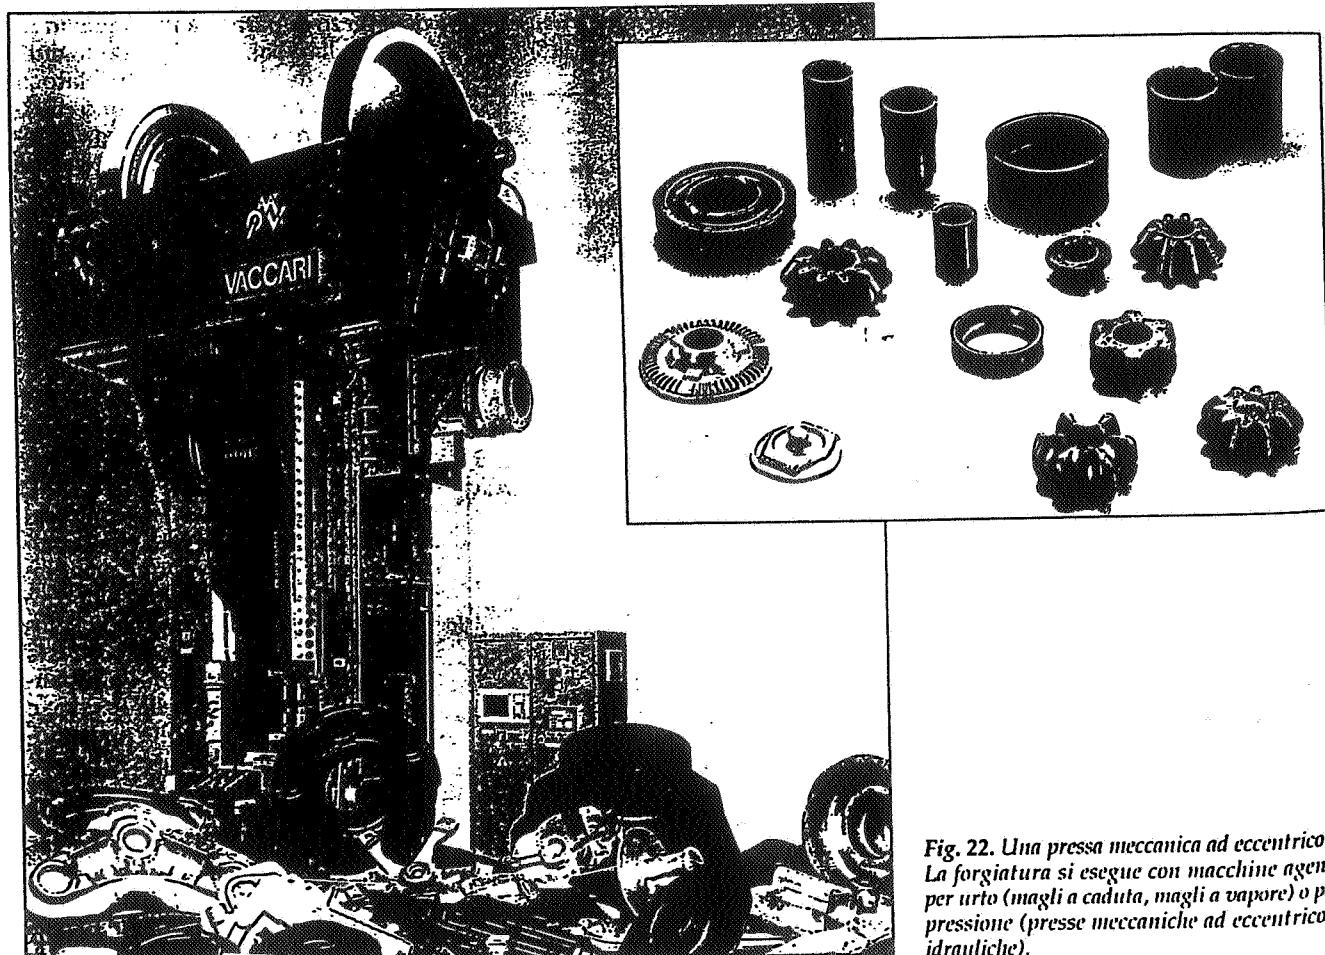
Una presa meccanica ad eccentrico. La forgatura si esegue con macchine agenti per urto (magli a caduta, magli a vapore) o per pressione (presse meccaniche ad eccentrico o idrauliche).
